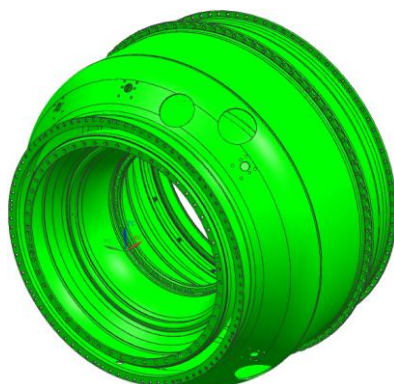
Трёхмерная модель корпуса КС в сборе
